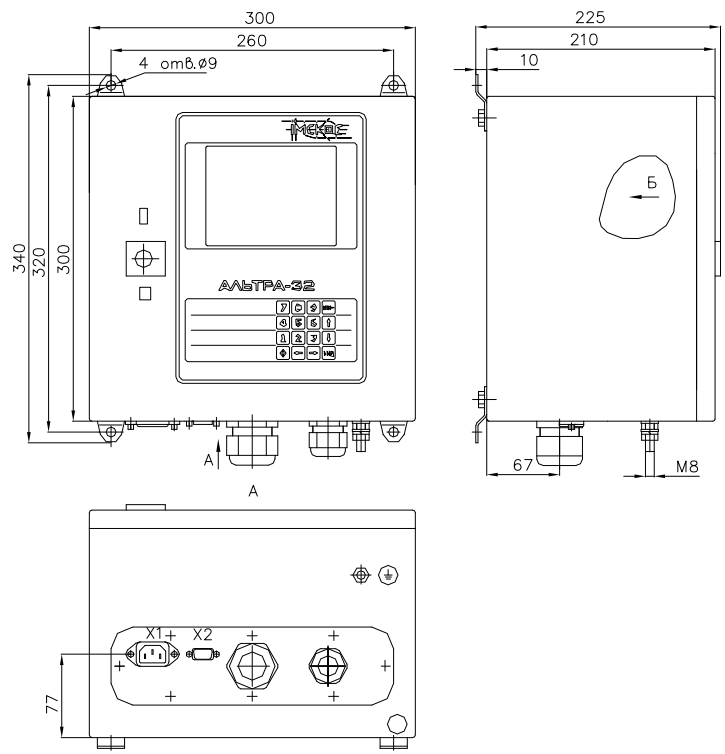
Габаритні розміри пристрою АЛЬТРА32-*16
